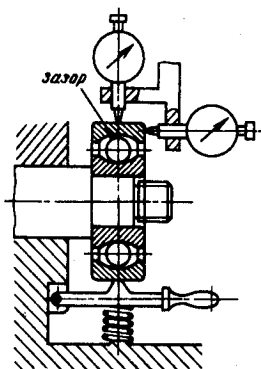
Схема приспособления для проверки радиального зазора в шарикоподшипнике после его напрессовки на вал
